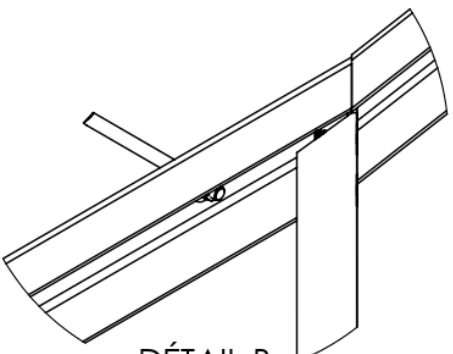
DETAIL ASSEMBLAGE CHENEAU ET POTEaux REP: ES4
